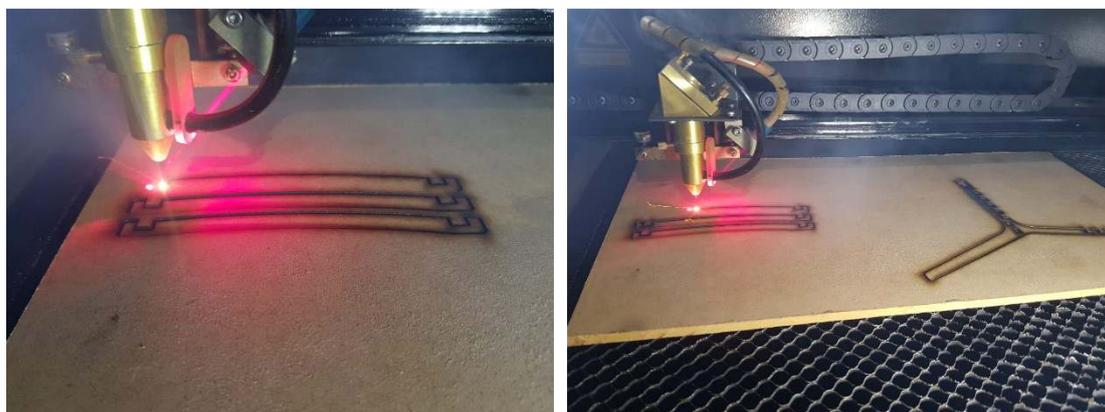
Processo de corte em cortadora a laser CNC; Fonte: Autora.
